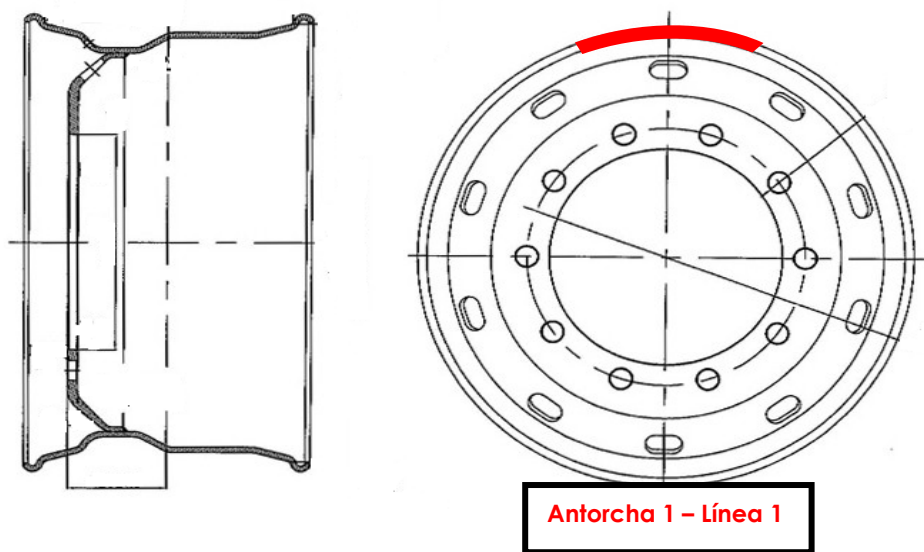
Esquema de posición de cordones de soldadura.
